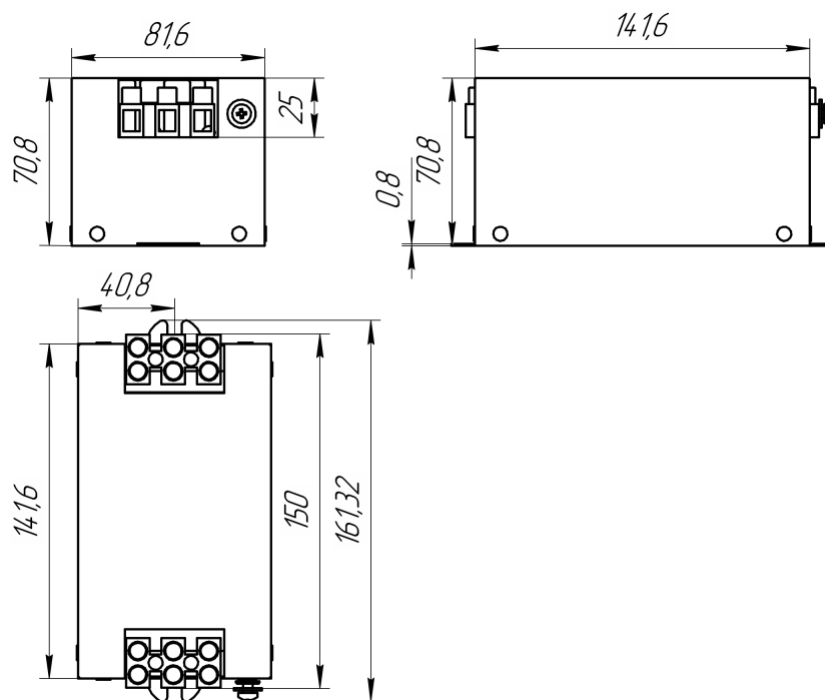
Габаритные размеры фильтра ФП-ВТ-3030
